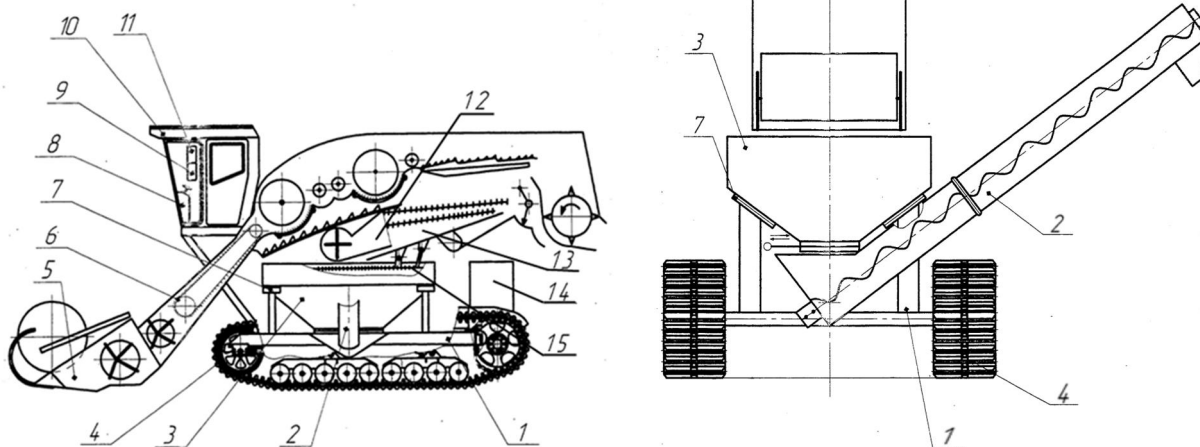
Комбайн самоходный гусеничный зерноуборочный новой компоновки (вид сбоку):
